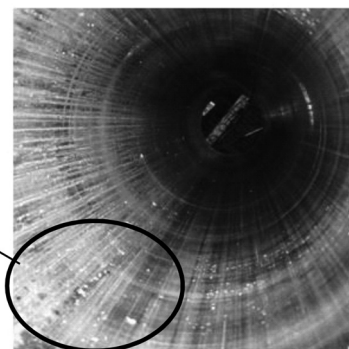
Царапины и следы коррозии на поверхности гильзы гидроцилиндра
